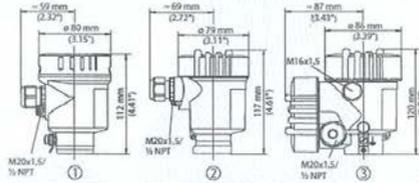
Корпус із нержавіючої сталі (1 – однокамерний корпус, електрополірований; 2 – однокамерний корпус, точне лиття; 3 – двохкамерний корпус, точне лиття)
